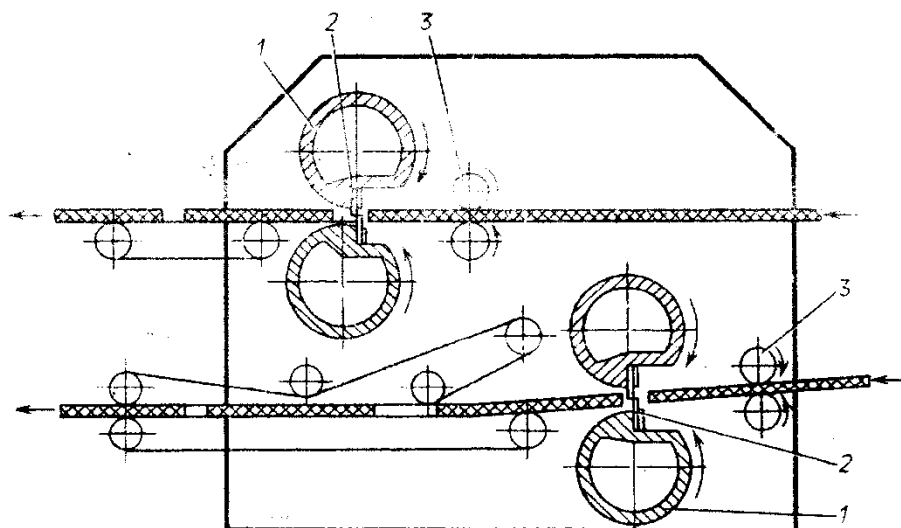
Схема двухъярусной поперечно-резательной машины:
